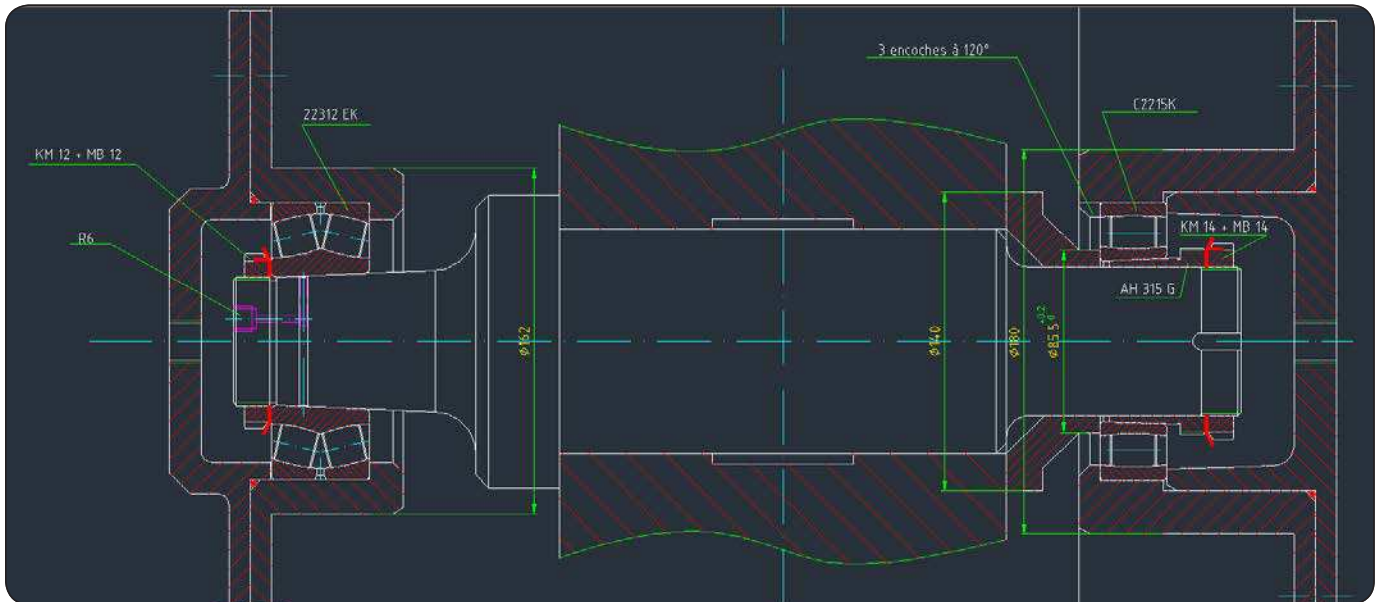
Disposición modificada de rodamientos de engranaje intermedio con un rodamiento de rodillos a rótula y un rodamiento de rodillos toroidales CARB. Ambos tienen ajustes apretados en sus aros interior y exterior. El diseño original contaba con dos rodamientos de rodillos a rótula con ajuste flojo en los aros exteriores. Como el engranaje accionaba o era accionado, se producían cambios de sentido de la carga en los aros exteriores. Esto provocaba un desgaste debido a los microdesplazamientos y al deslizamiento de los aros exteriores en sus asientos.
